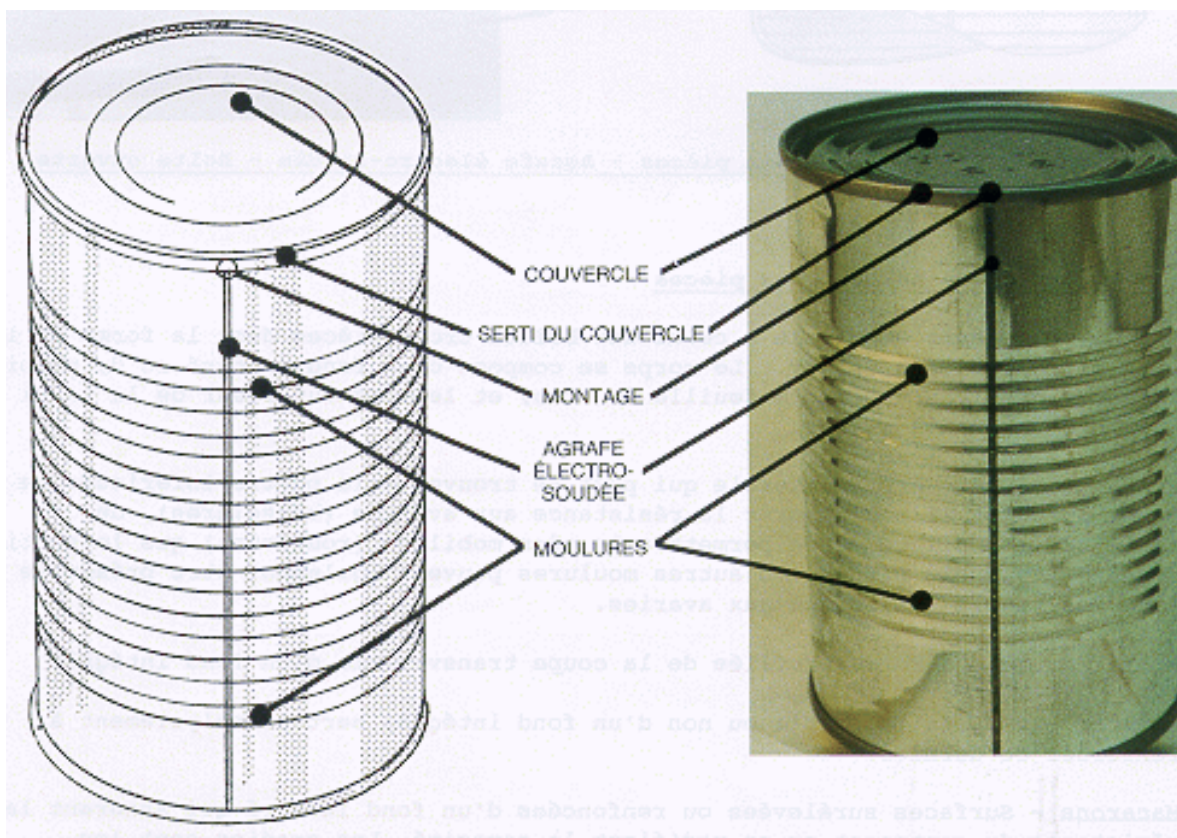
Boîte trois pièces - Agrafe électro-soudée - Boîte fermée
